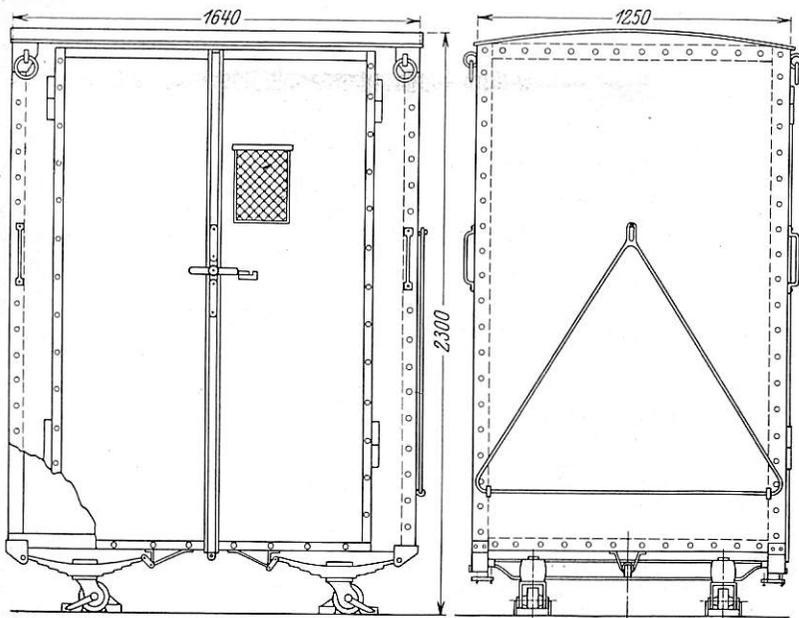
Beispielskizze für einen geschlossenen Behälter.
